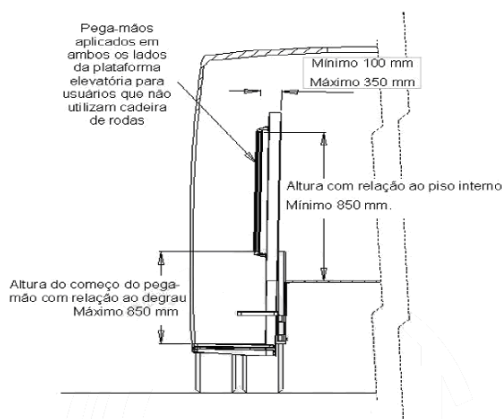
Pega-mão instalado na plataforma elevatória veicular.
